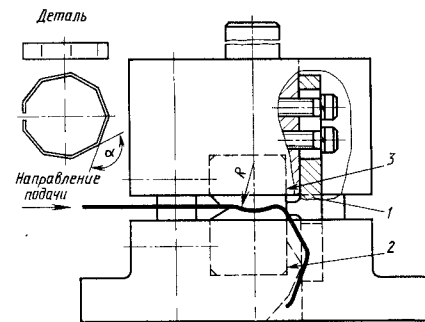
Штамповка многогранного кольца путем последовательного изгиба заготовки
